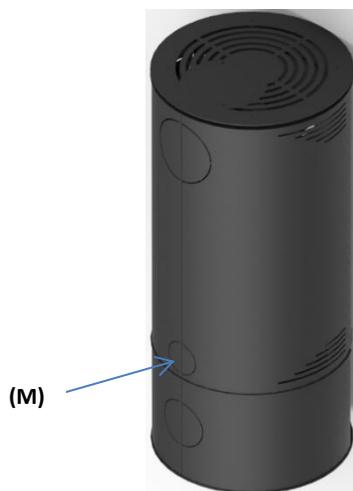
Vue arrière de l'équipement, section à supprimer pour l'entrée d'air extérieur
